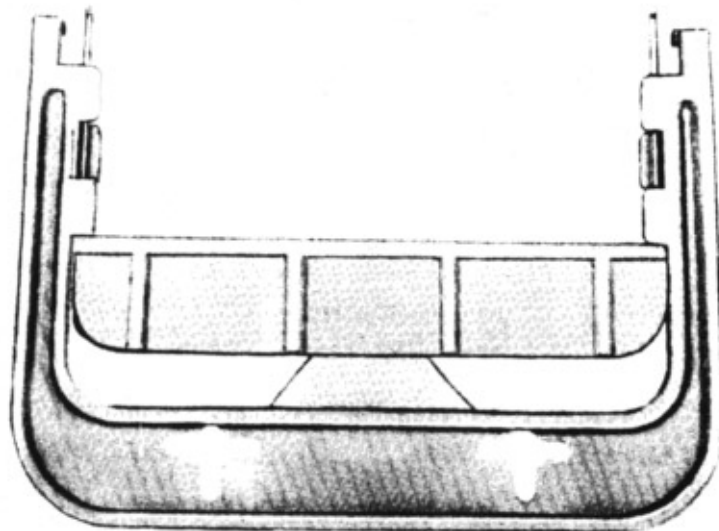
(8043016) Herramienta para extracción de tarjeta de circuito impreso
